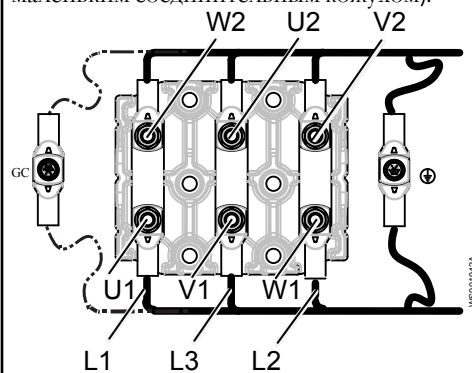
2 кабеля, приводы 605/615, 665/675; 705/715, 735/745, 765/775
